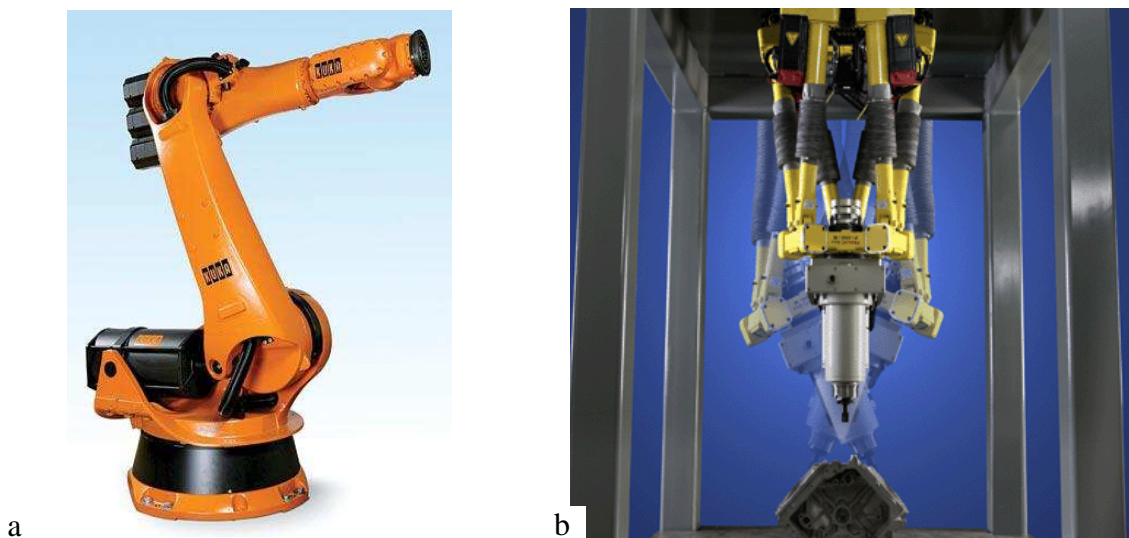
a) robot d'usinage sériel KUKA b) robot d'usinage parallèle FANUC F-200iB
